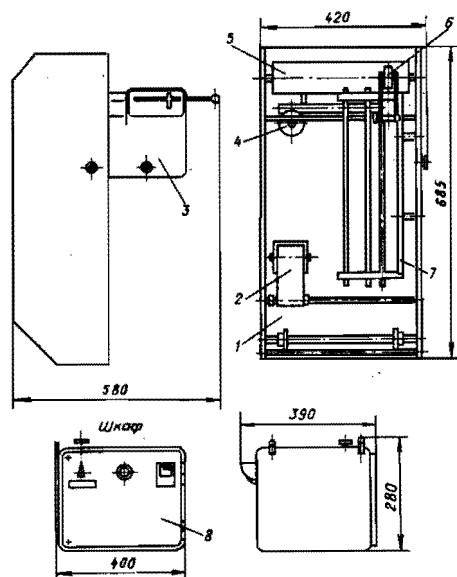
Общий вид устройства аппликаторного марки Д9-ОАА:
